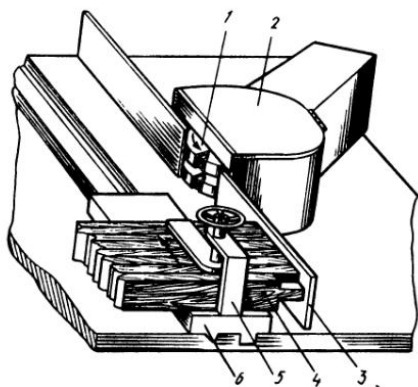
Формирование прямых рамных шипов на фрезерном станке:
